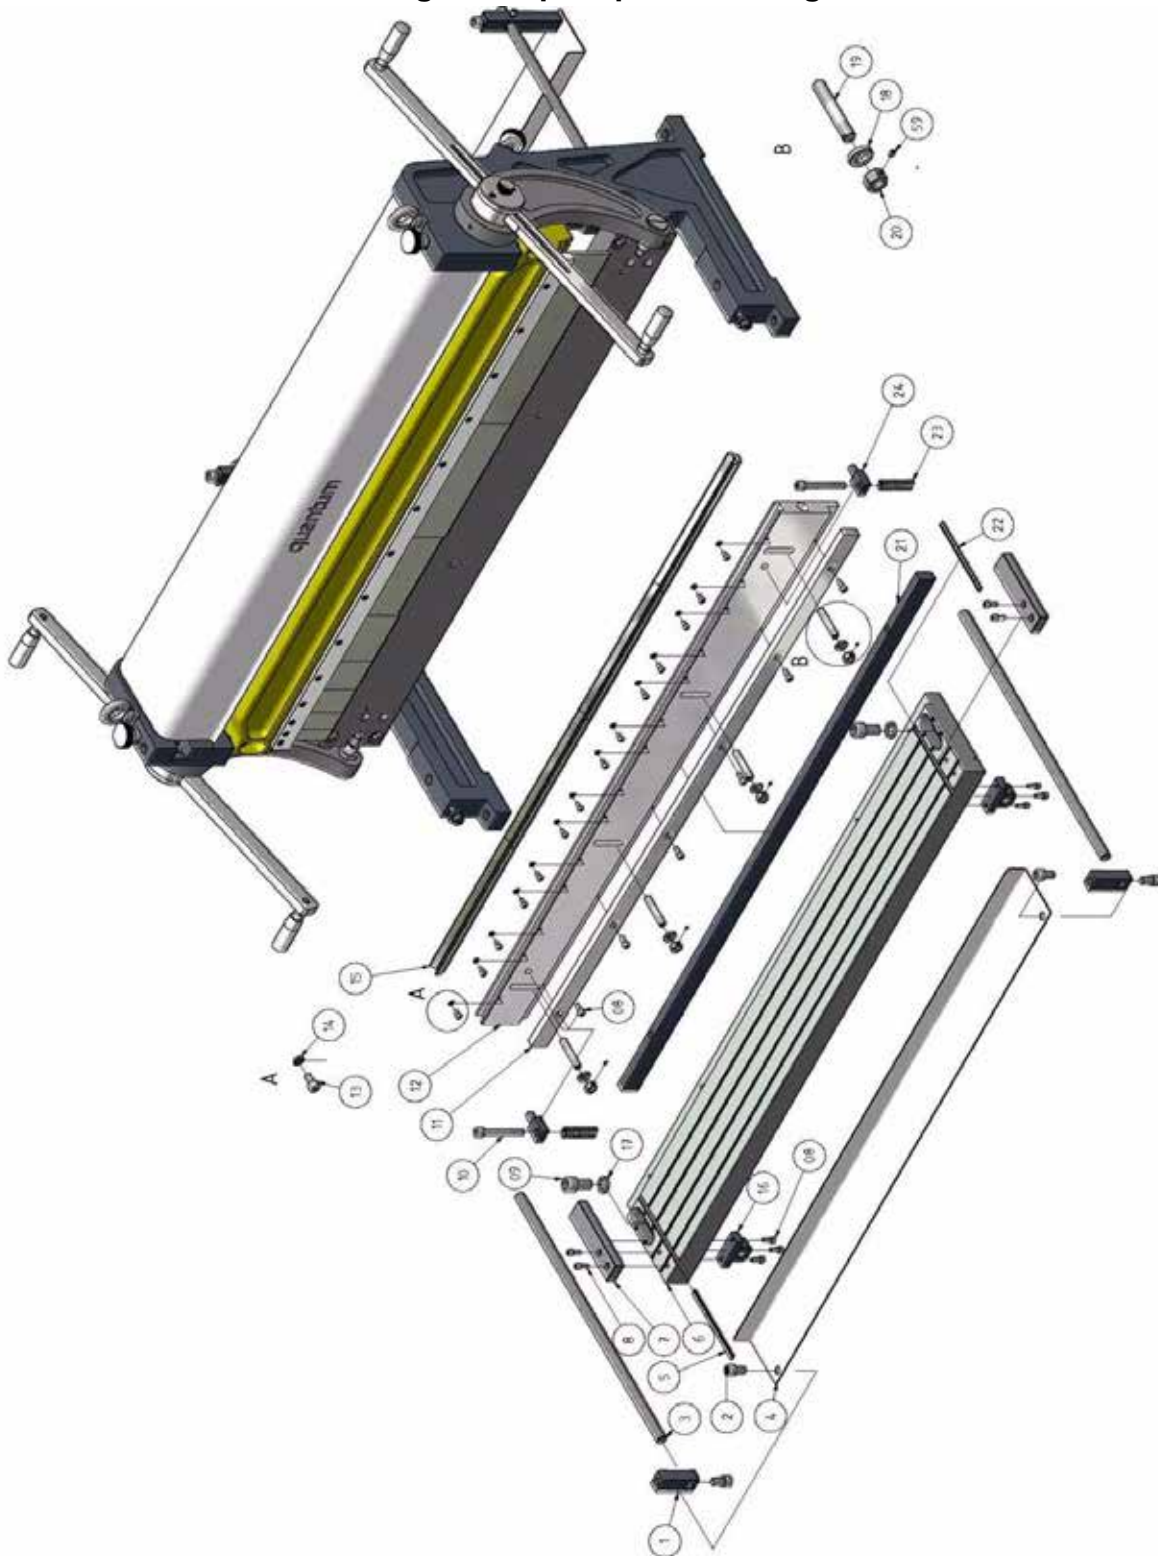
Ersatzteilzeichnung 1-4 - Drawing spare parts 1-4
